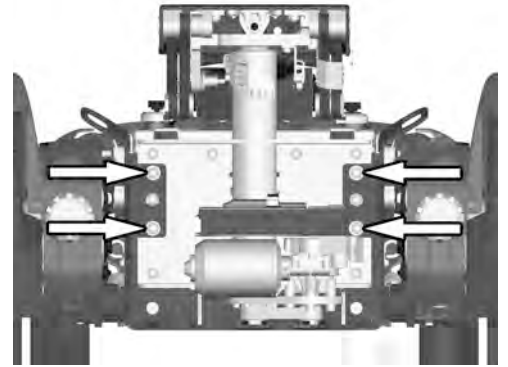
Die vorderen Transportösen sind mit jeweils zwei Schrauben befestigt.
